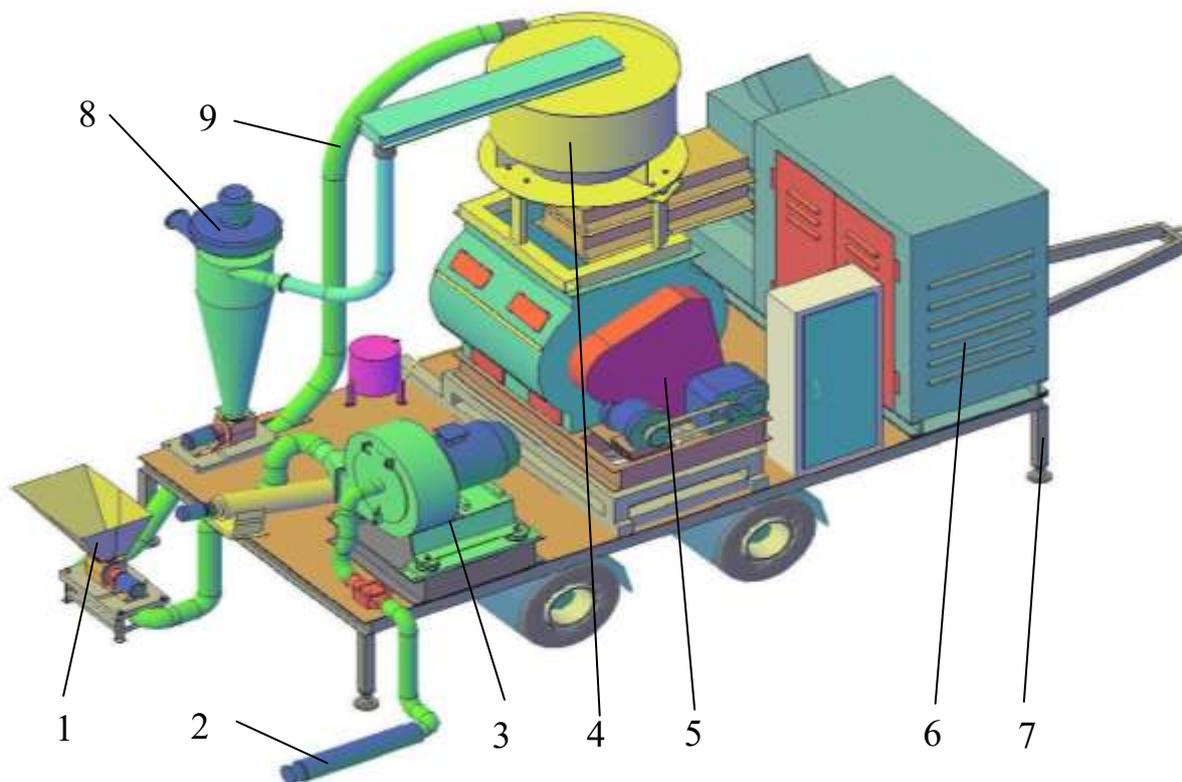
Мобильная установка «ВНИИКП» для приготовления полнорационных комбикормов в хозяйствах (схема устройства): 1 – приемная воронка для загрузки БВМК; 2 – всасывающий патрубок; 3 – молотковая дробилка; 4 – надсмесительный бункер; 5 – горизонтальный смеситель; 6 – электрогенератор; 7 – шасси; 8 – циклон; 9 – нагнетательный патрубок
